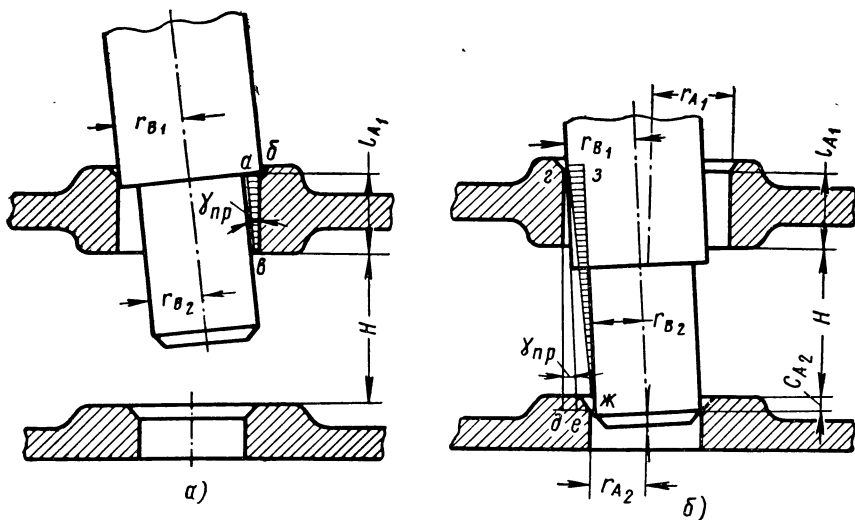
Схема для расчета условий сборки по методу регулировок для многоопорного вала (втулки) с корпусом
